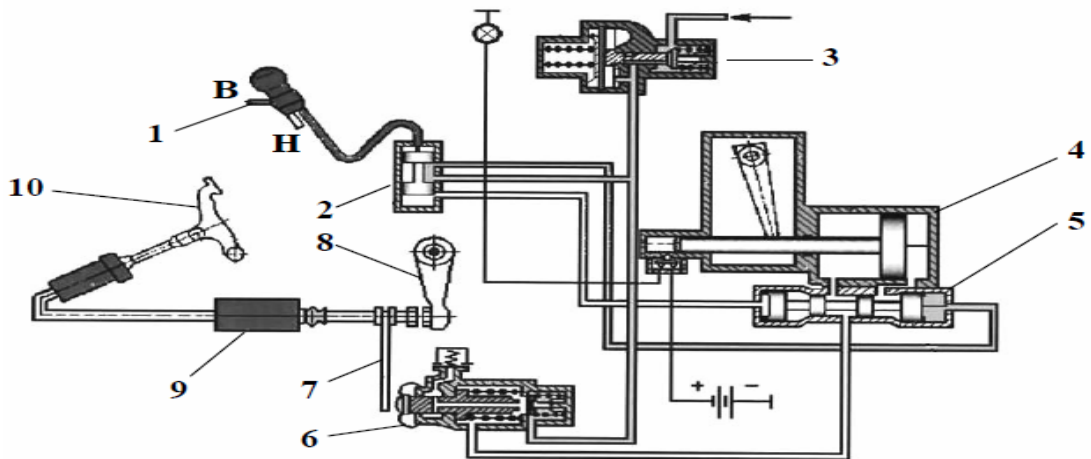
Схема пневматической системы управления делителем передач:
